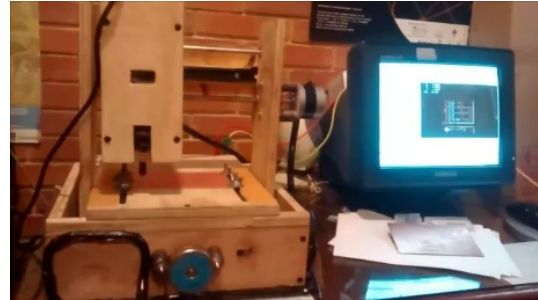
Parte 1 - Máquina fresadora CNC elaborando una PCB
